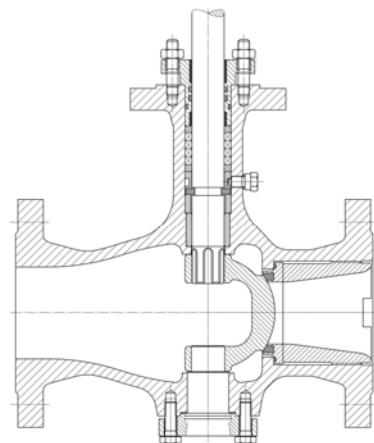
Maxifluss Rotary Plug Valve VETEC-Type 72.3 MN DVGW
